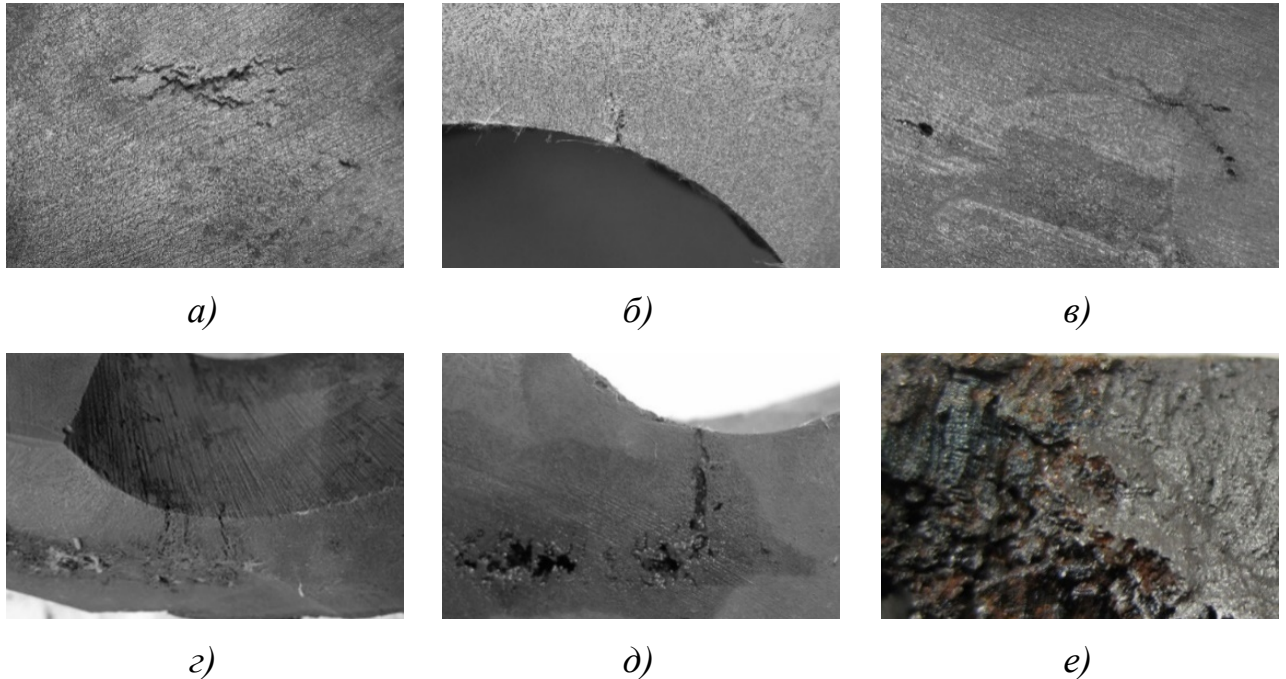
Дефекты второй группы, имеющие смешанную газо-усадочную природу образования: а, в – наружная поверхность отливок (травлена), $\times 2$; б, г – поперечный разрез стенки отливки в месте образования дефекта (травлено), $\times 2$; д – поперечный разрез стенки отливки в месте образования дефекта (травлено), $\times 2$; е – излом стенки, $\times 5$
